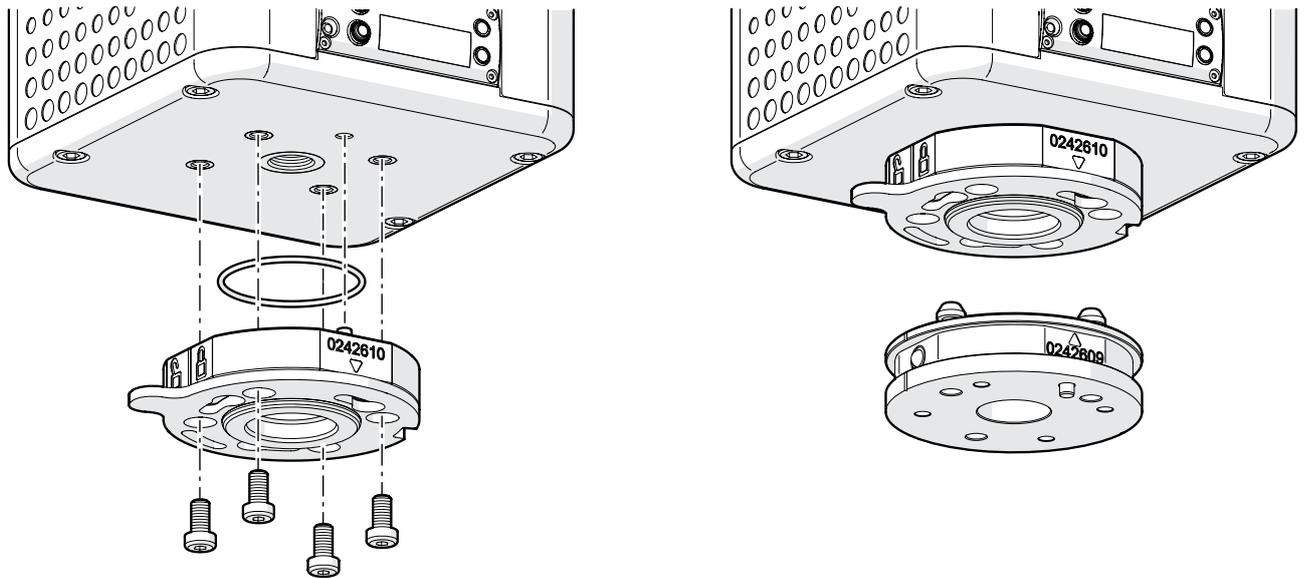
Der Werkzeugwechsler ist am piCOBOT® Electric befestigt.
